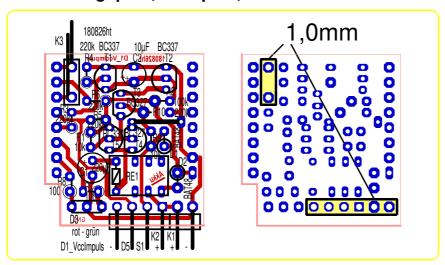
Bestückung und Bohrplan des VccImpuls-Shields Alle Bohrungen 0,8mm außer K1, K2, K3 (1mm)
